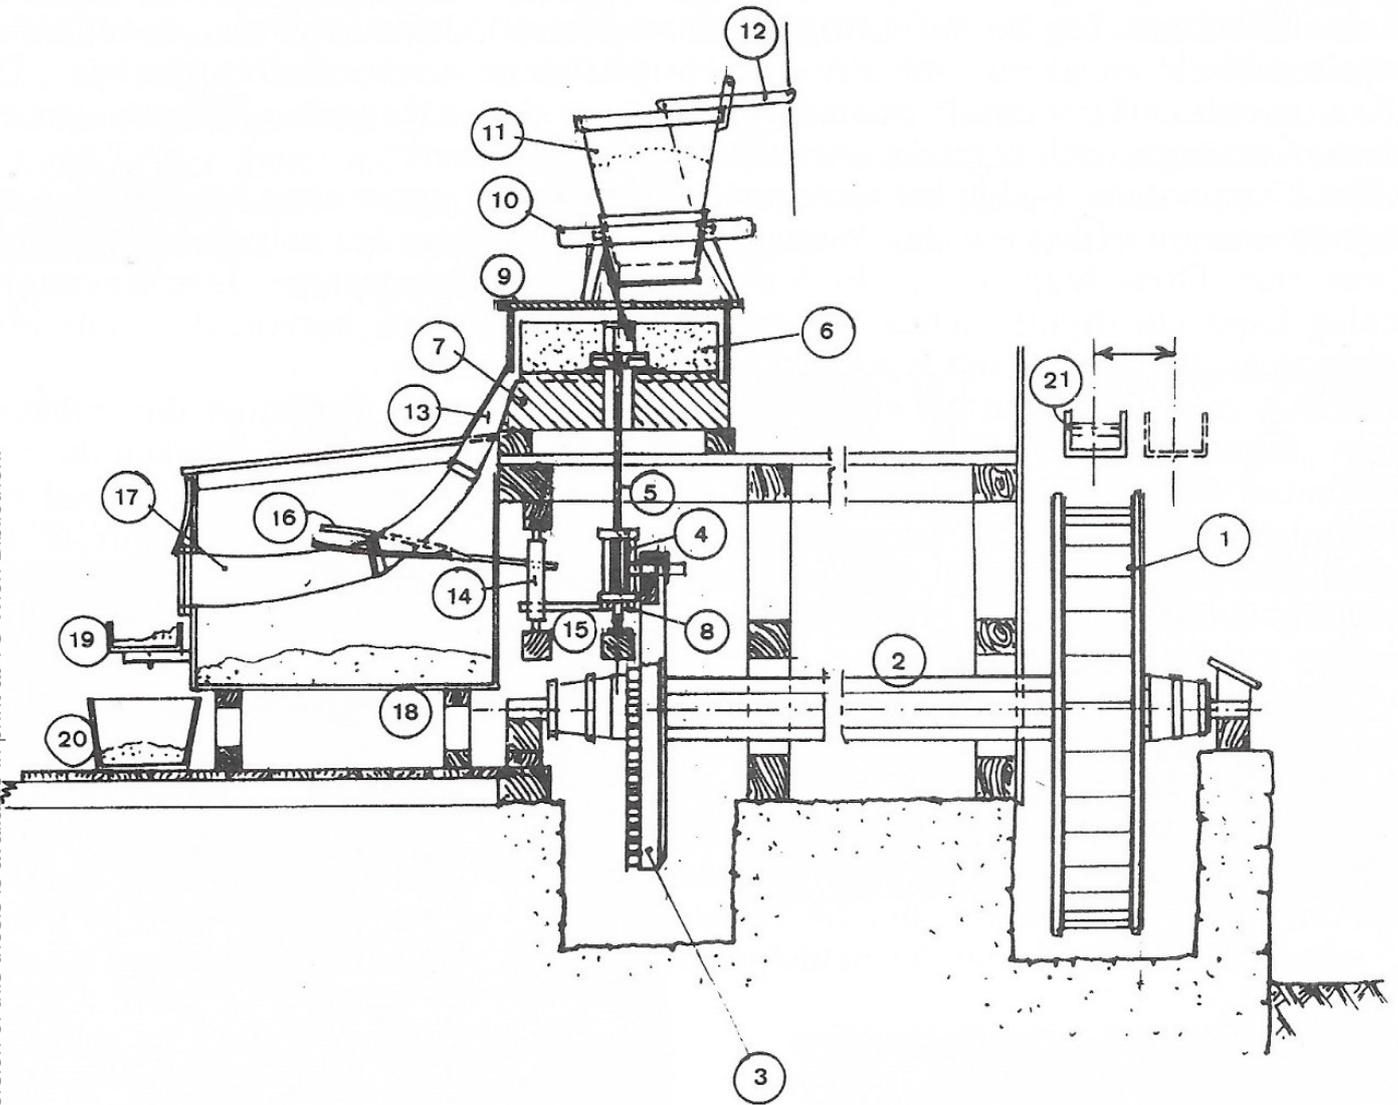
Schemaschnitt durch eine eingängige Wassermühle mit Oberschlächtigem Wasserrad.
